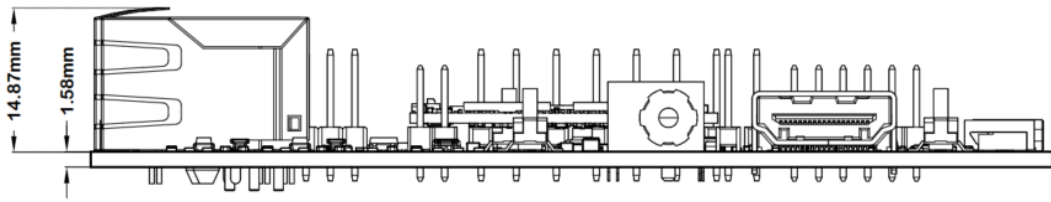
DEI60F225-EVB 侧面尺寸 (单位: mm)
